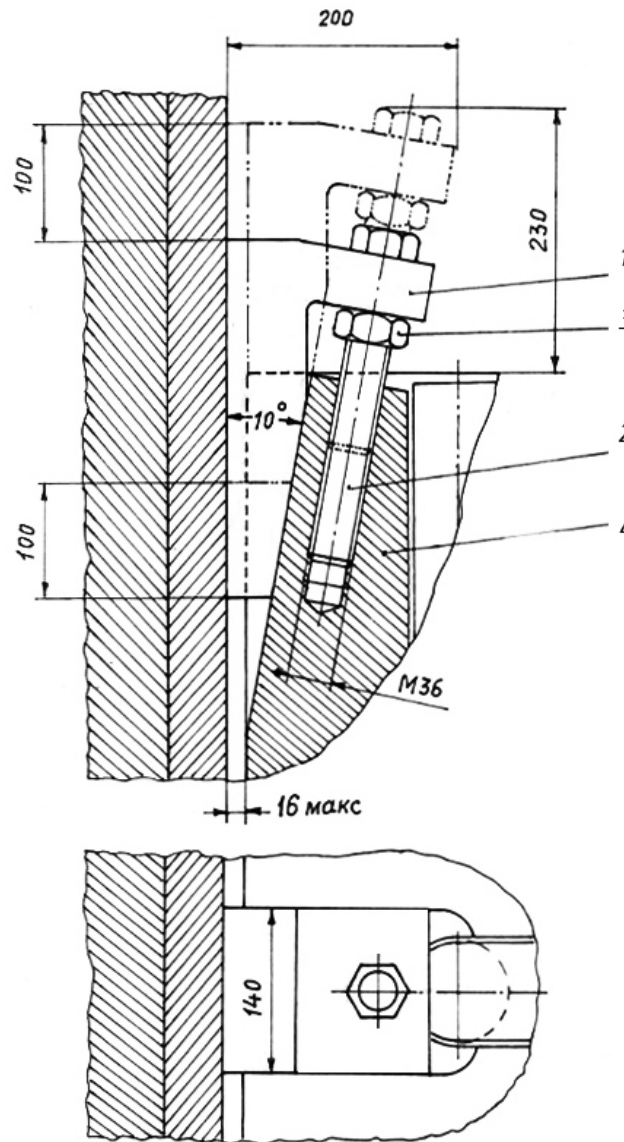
Клиновий пристрій подушки верхнього валка
